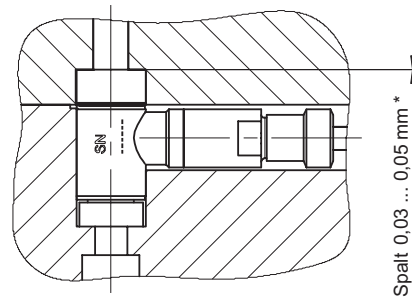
Einbaubohrung mit Druckscheibe Typ 9413
